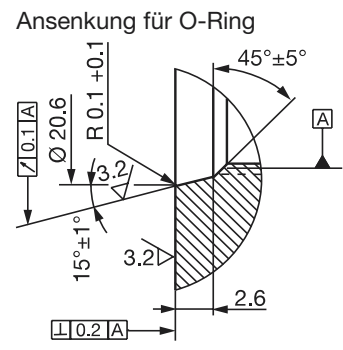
Einschraubloch für die Montage des BTL mit O-Ring
